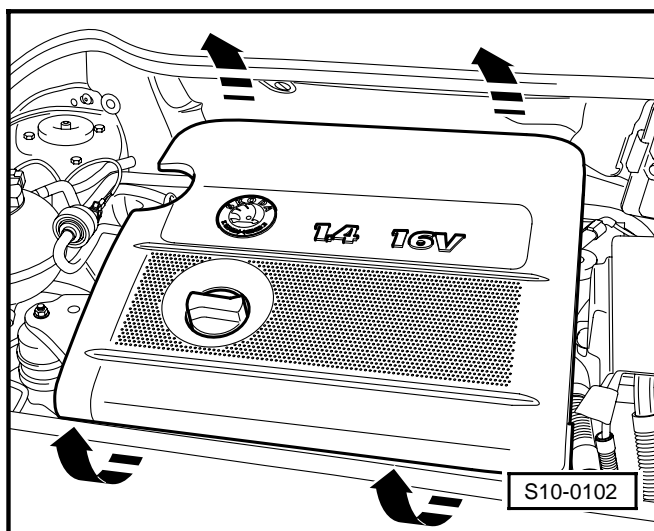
Demontáž a montáž krytu motoru se vzduchovým filtrem
